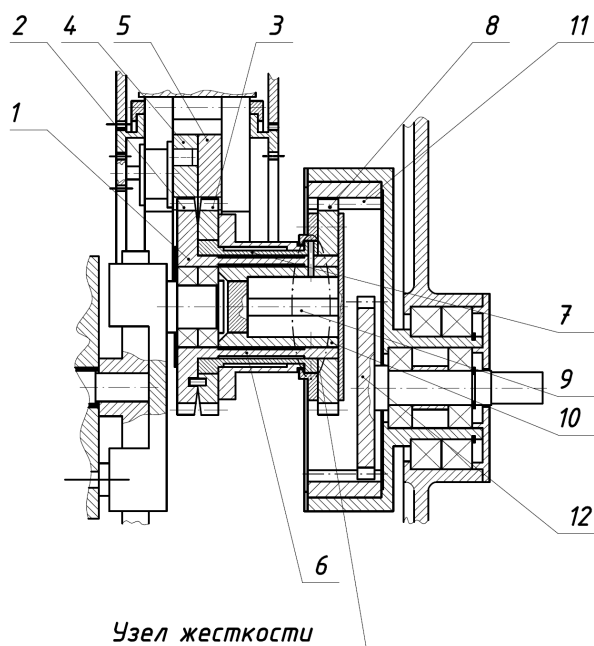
Конструкция компенсатора погрешности угла поворота сателлита
